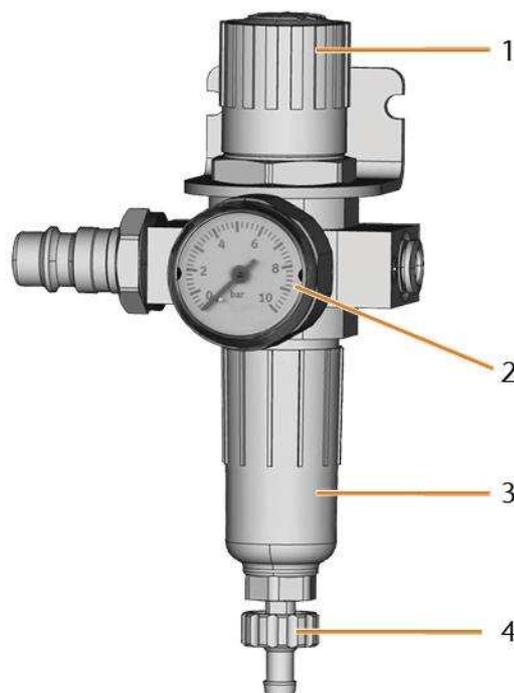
DRUCKMINDERER: DRUCKLUFT EINSTELLEN UND KONTROLLIEREN
